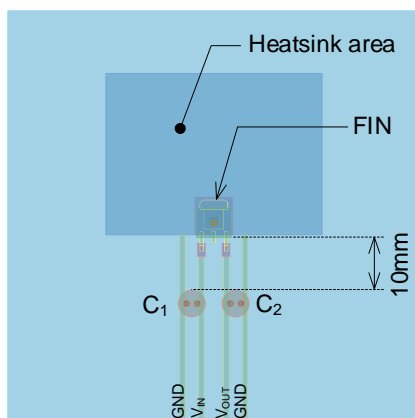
将电容器与散热区分开布置的 PCB Layout
